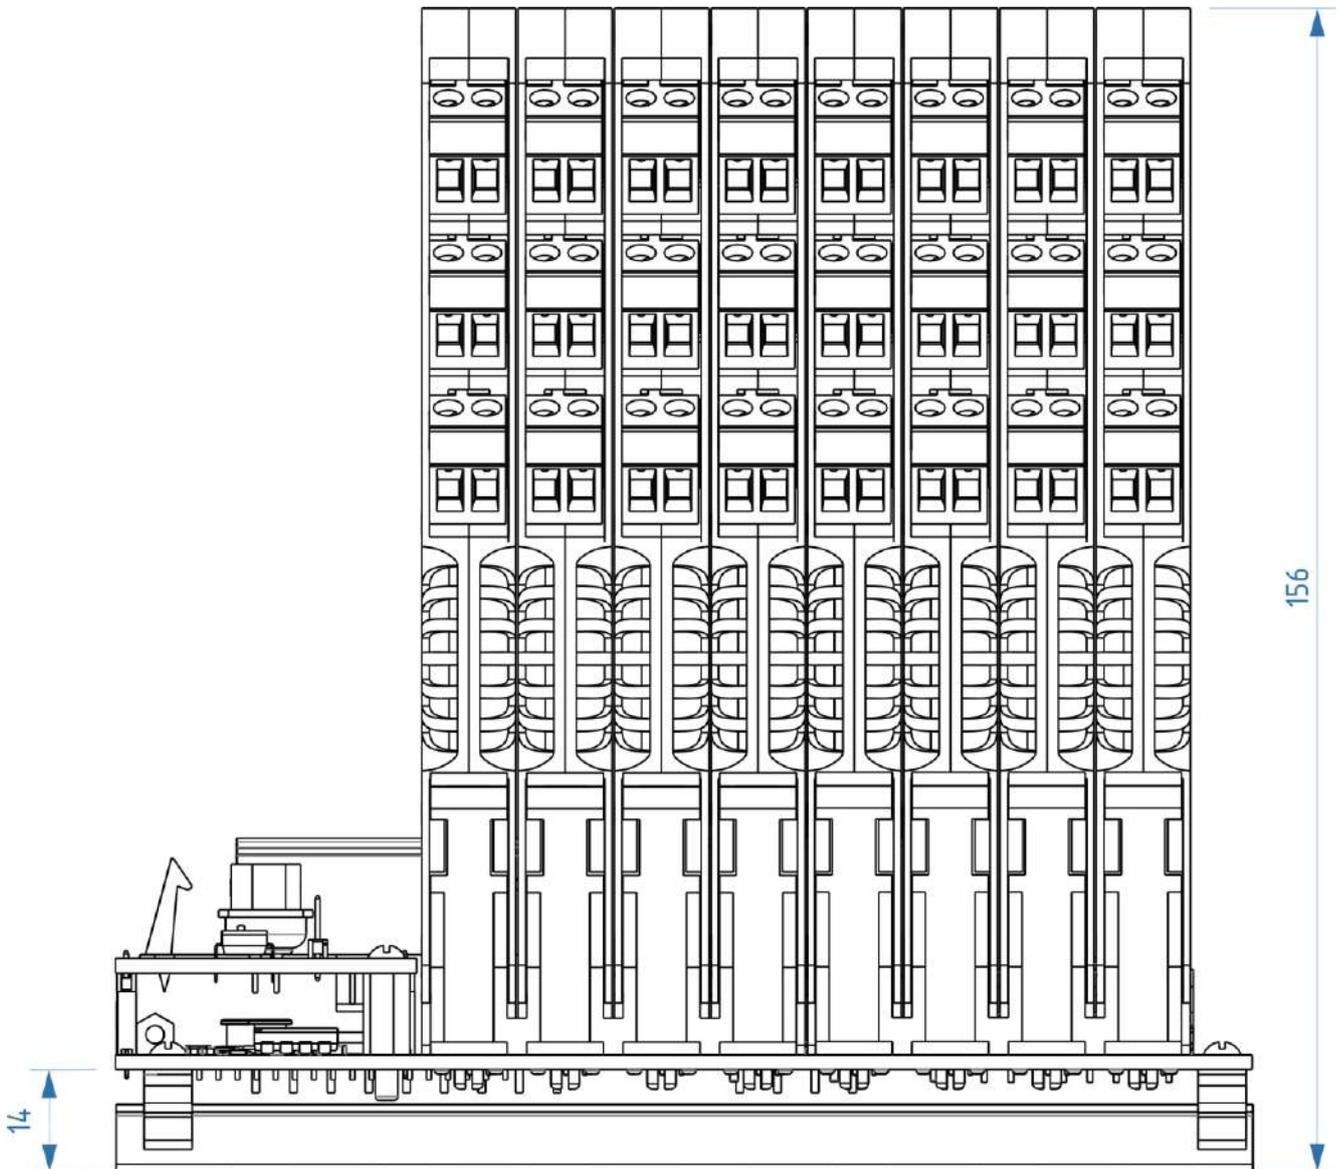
Габаритные размеры ЛПА-300-х02 с установленными барьерами искробезопасности и крепежом на DIN-рейку
